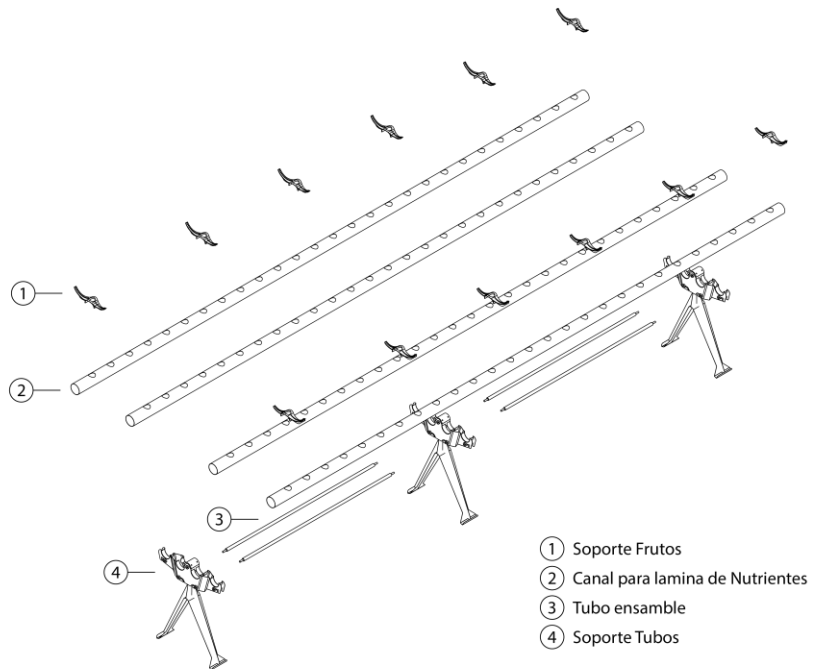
Módulo de plantación (MPL). Armado. Elaboración propia (2014).
